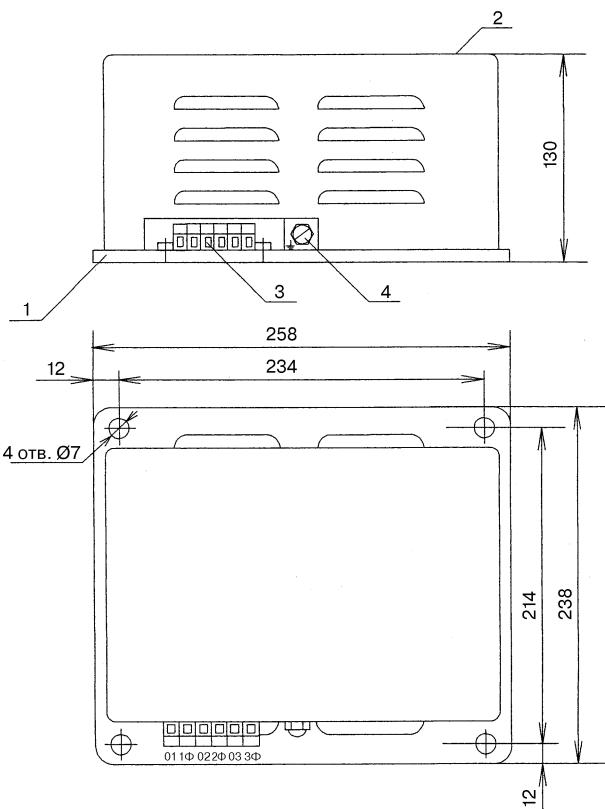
Внешний вид блока Б3П3-25 и Б3П3-100, где: 1 — основание; 2 — кожух; 3 — клеммной соединитель; 4 — винт заземления
